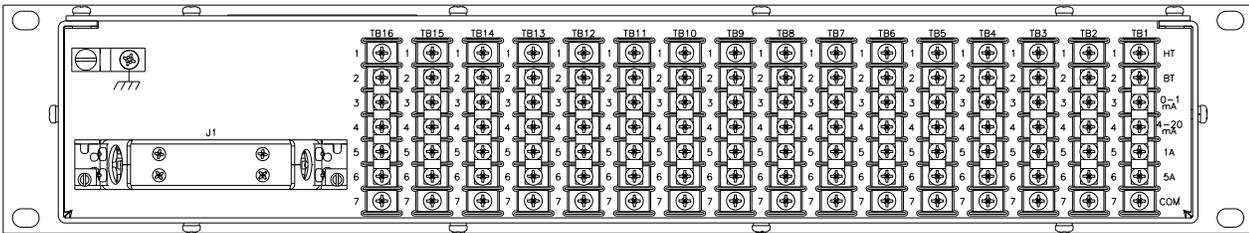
Vue arrière du module 2UM, modèle MS16-2UM, sans support de câbles
